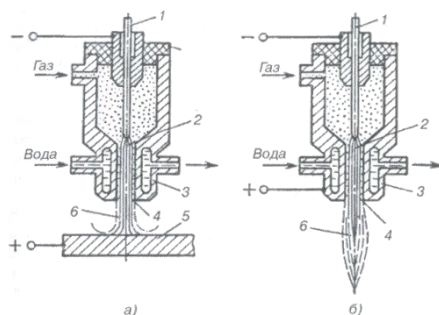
Схема сварки плазменной дугой: *а* - прямого действия; *б* - косвенного действия; 1 - вольфрамовый электрод; 2 - дуга; 3 - сопло горелки; 4 - канал сопла; 5 - изделие (заготовка); б - плазменная дуга
